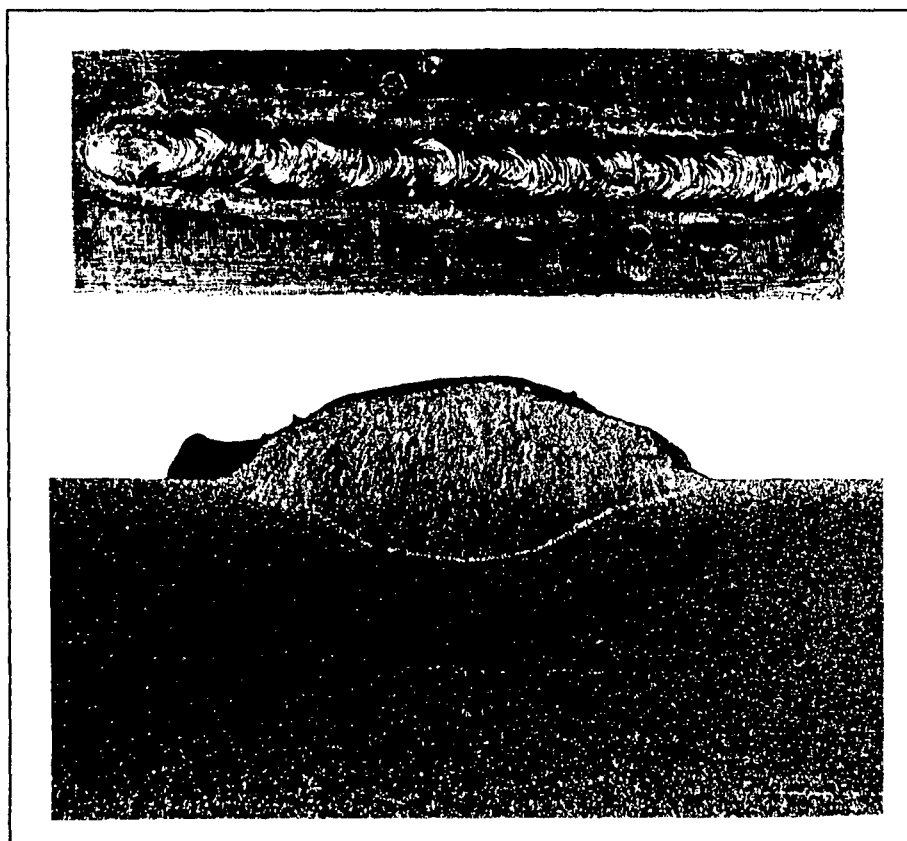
Aspecto do cordão de solda para o eletrodo D em CA.
